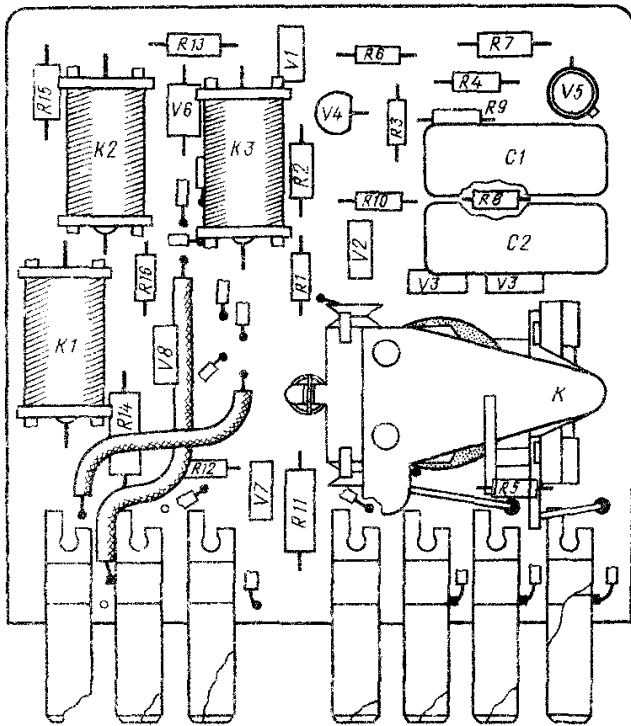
Расположение деталей реле-прерывателя указателей поворота и аварийной сигнализации
